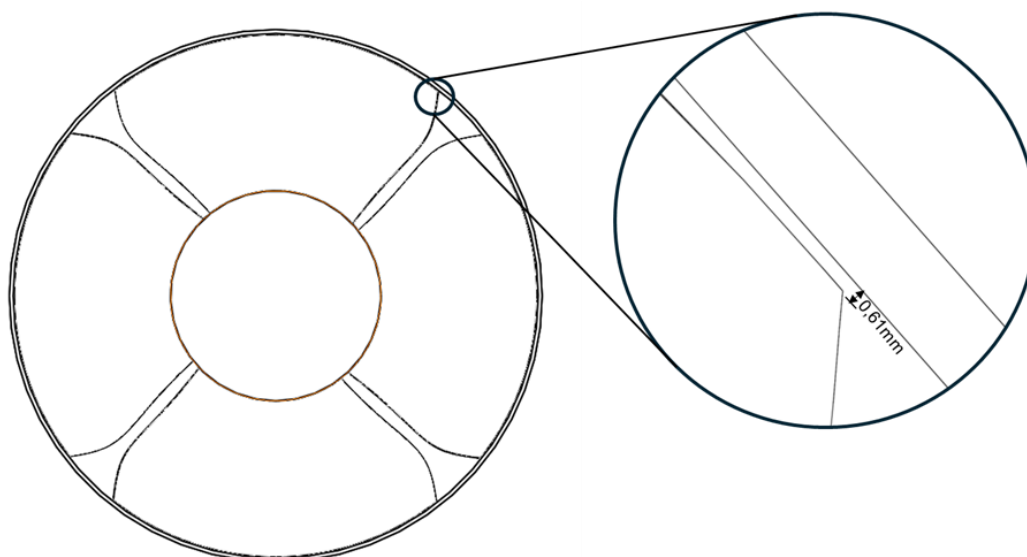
Vista frontal montagem rotor com detalhe no gap.
